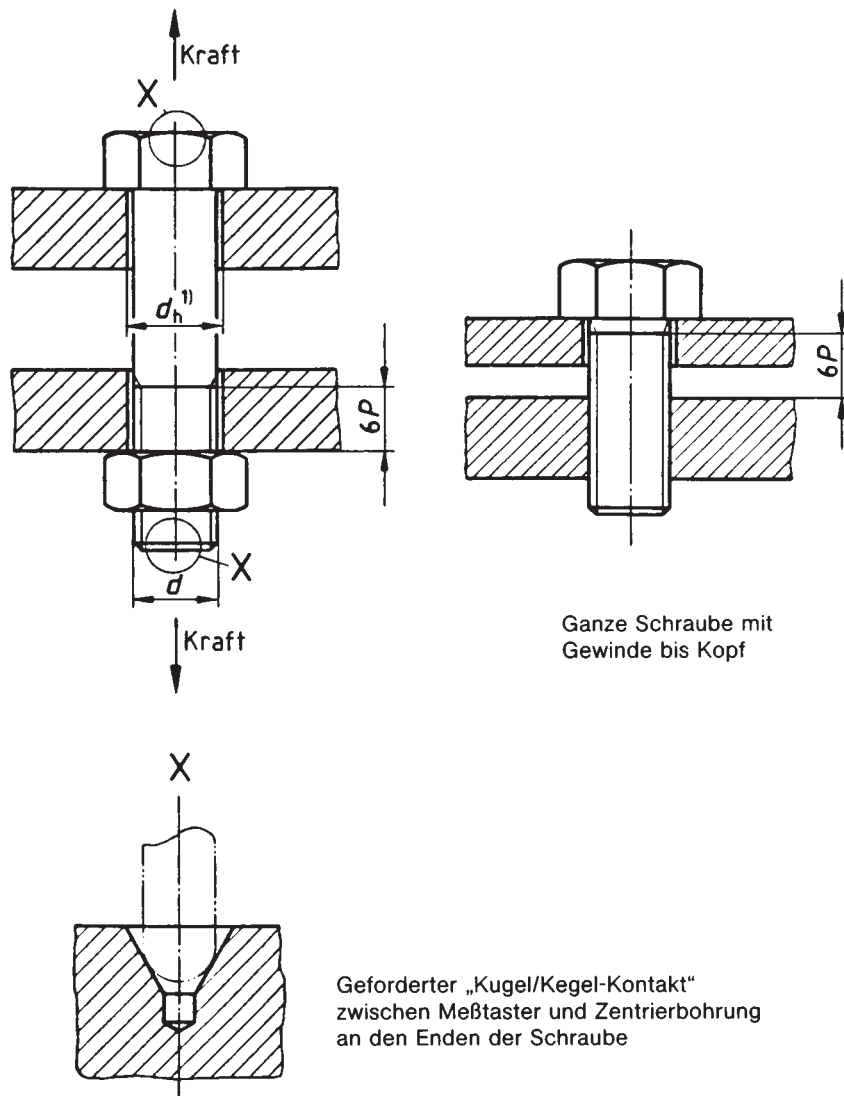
Aufbringen der Prüfkraft auf ganze Schrauben
